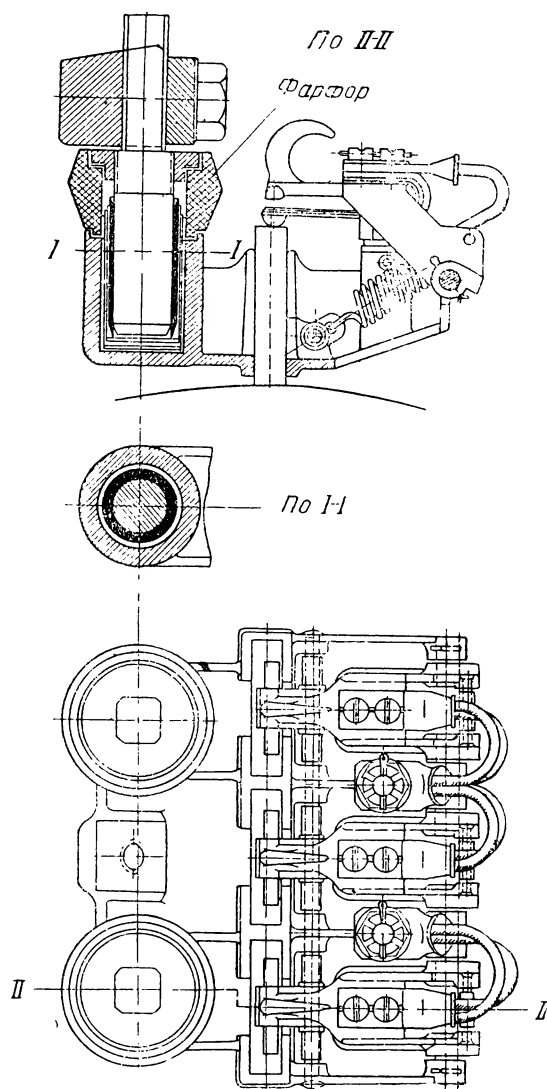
Щеткодержатель шахтного тягового двигателя.
